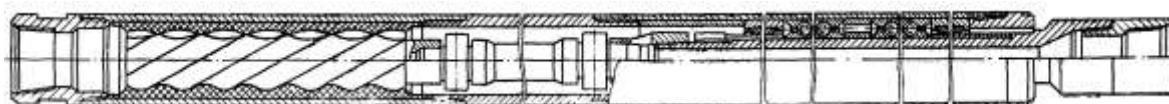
Винтовой забойный двигатель типа Д
